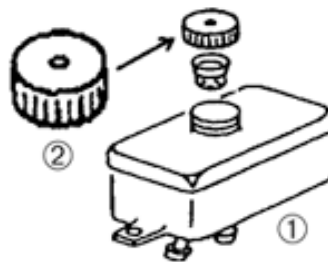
Bomba de Freno. Fuente (www.serca.es.com).
